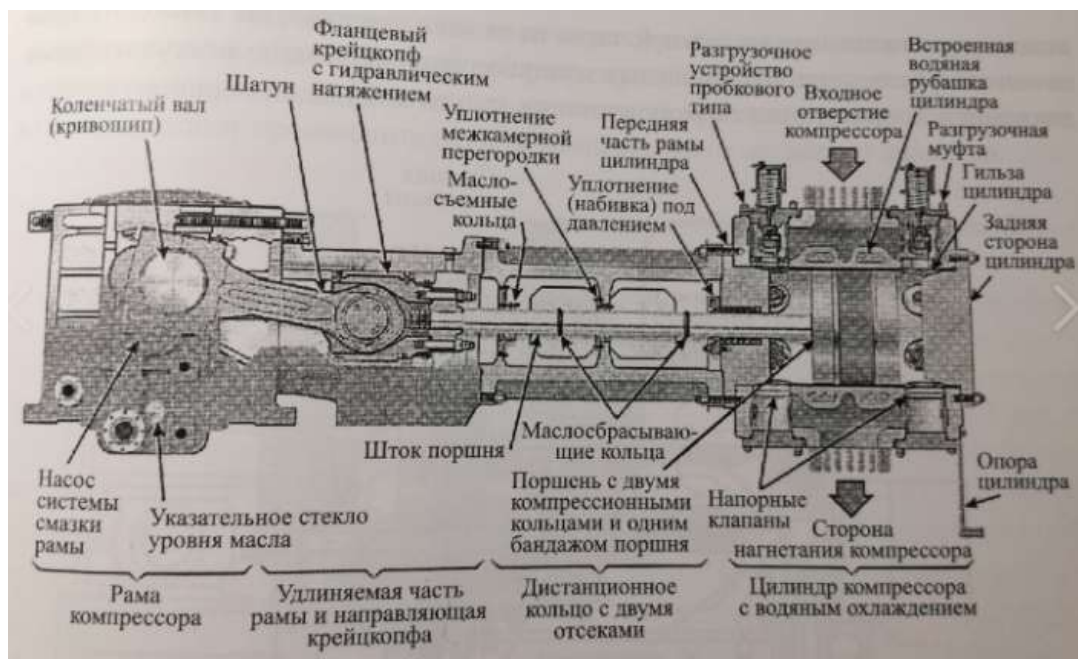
Компоненты поршневого компрессора с возвратно-поступательным движением поршня. [11]
